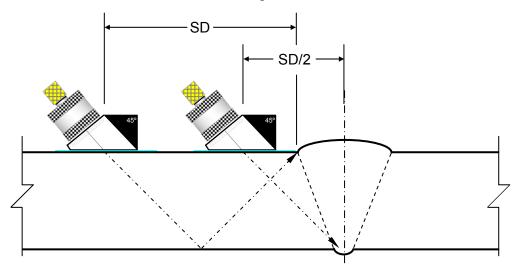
Inspección de un cordón de soldadura con palpador de haz angular
